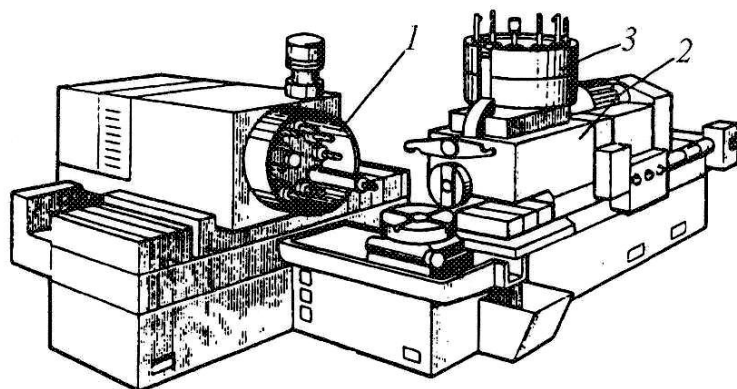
Агрегатний верстат з автоматичною зміною інструмента за програмою
